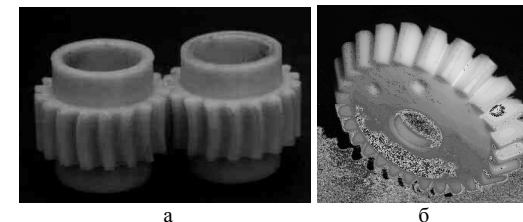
Циліндричні колеса з гвинтовими зубцями (а) і конічне прямозубе колесо (б), нарізані дисковою фрезою на зубофрезерному верстаті
